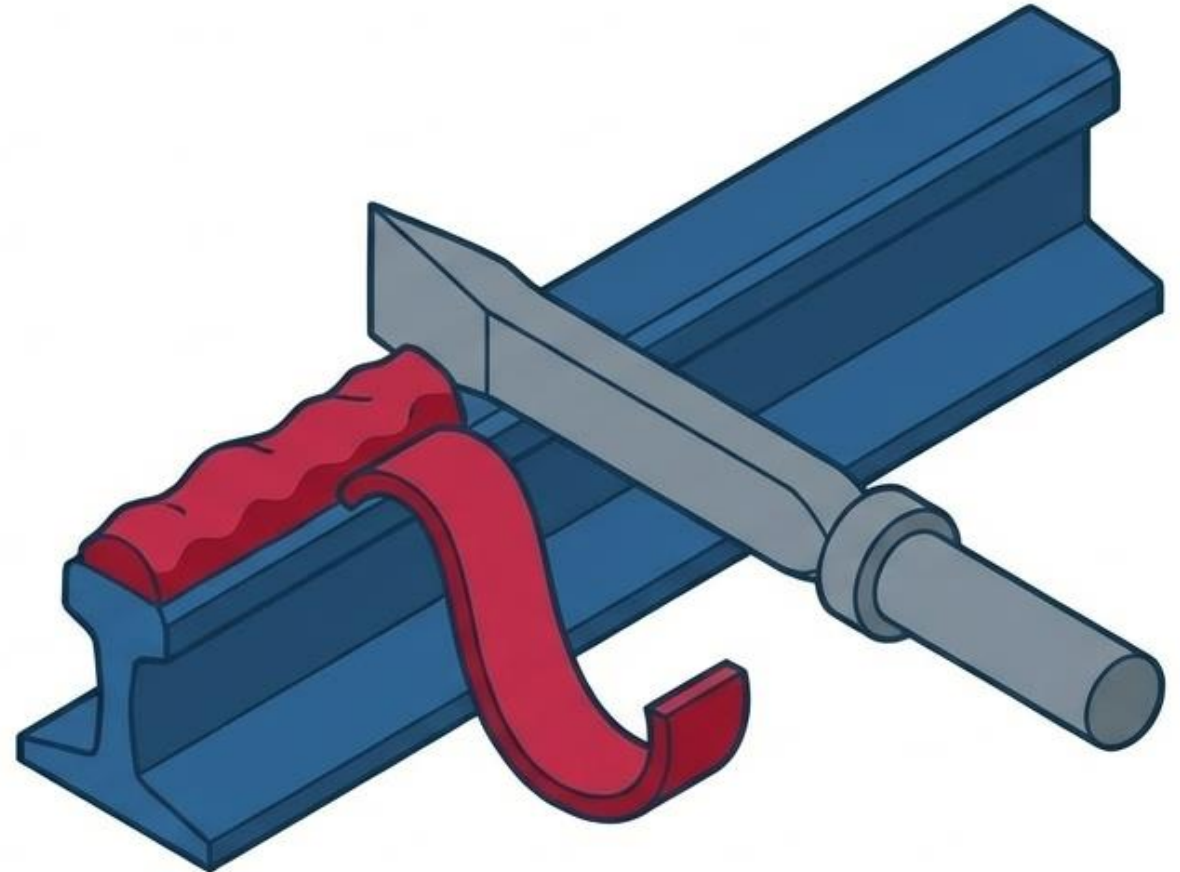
Soldadura aluminotérmica, colada.
